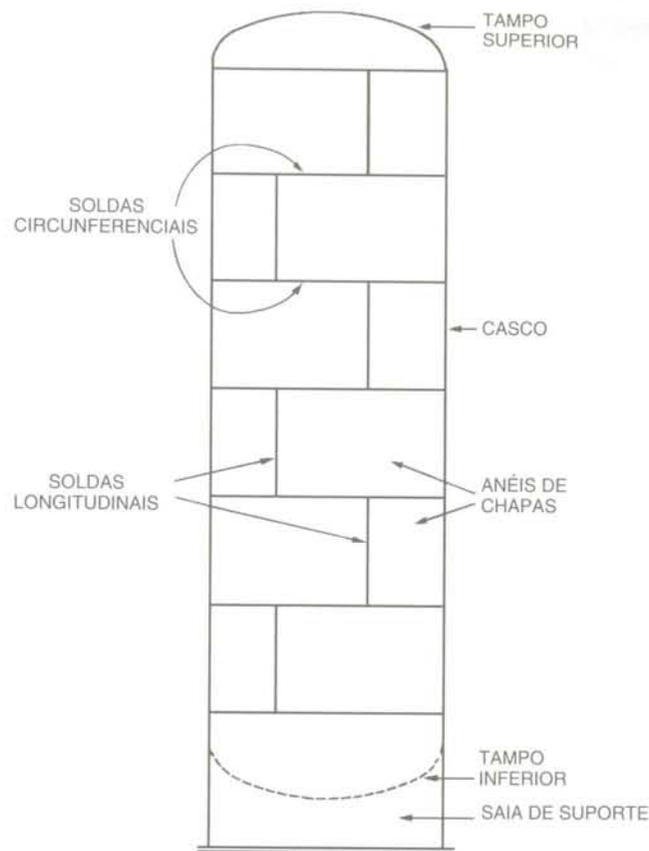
Soldas circunferenciais e longitudinais em um casco cilíndrico.
